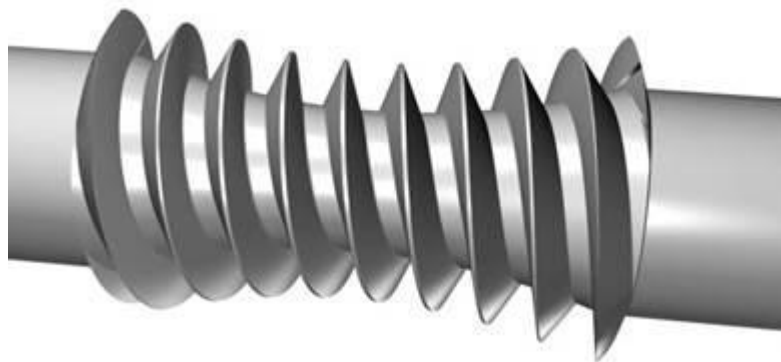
Схеми форм початкової поверхні черв'яка
